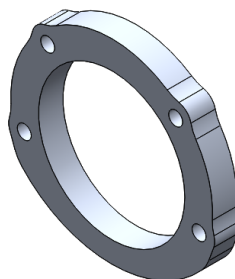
Vista isométrica de la pieza asiento de rodamiento
